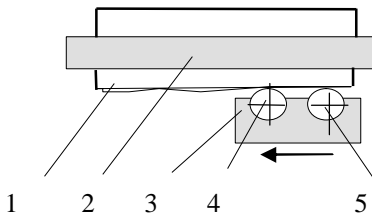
Схема работы кромко-фуговального станка КФ-9М: 1 - пачка шпона, 2 - прижимная траверса, 3 - каретка, 4 - обдирочная фреза, 5 - чистовая фреза
